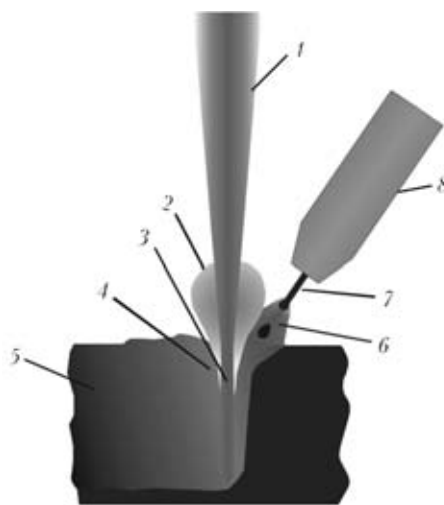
Схема гибридной лазерно-дуговой сварки: 1 — лазерный луч; 2 — плазма; 3 — парогазовый канал; 4 — жидкая ванна; 5 — свариваемый материал; 6 — сопло GMA; 7 — присадочная проволока; 8 — горелка GMA
